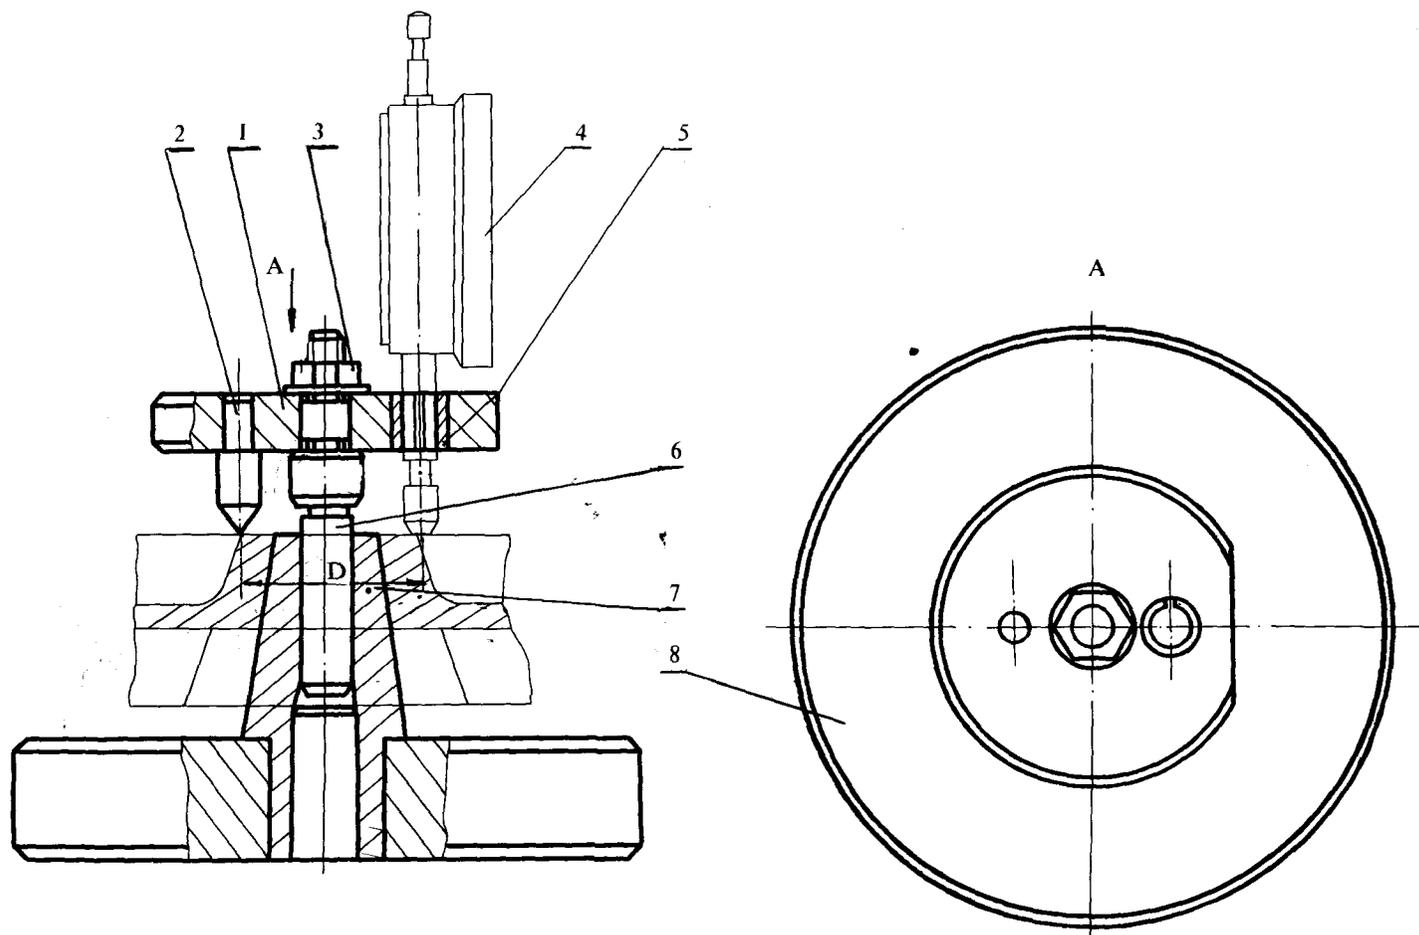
Контрольное приспособление для проверки биения торцов у дисков с коническим отверстием:
